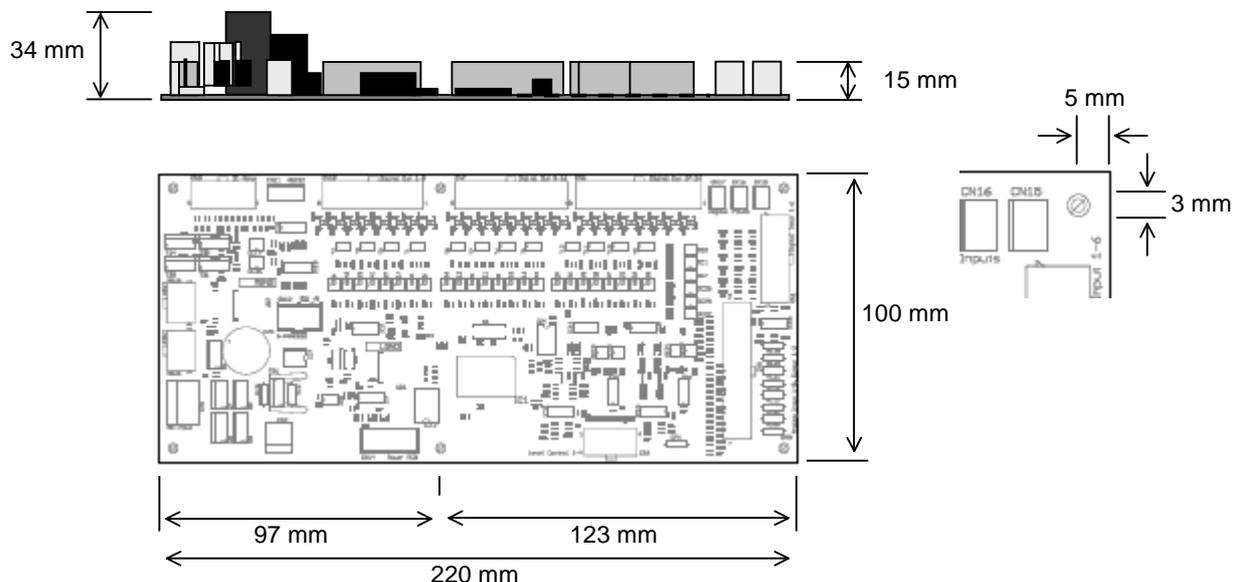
Abmessungen der universellen I/O-Karte FIOB (Aufriss, Grundriss und Lochmasse)
